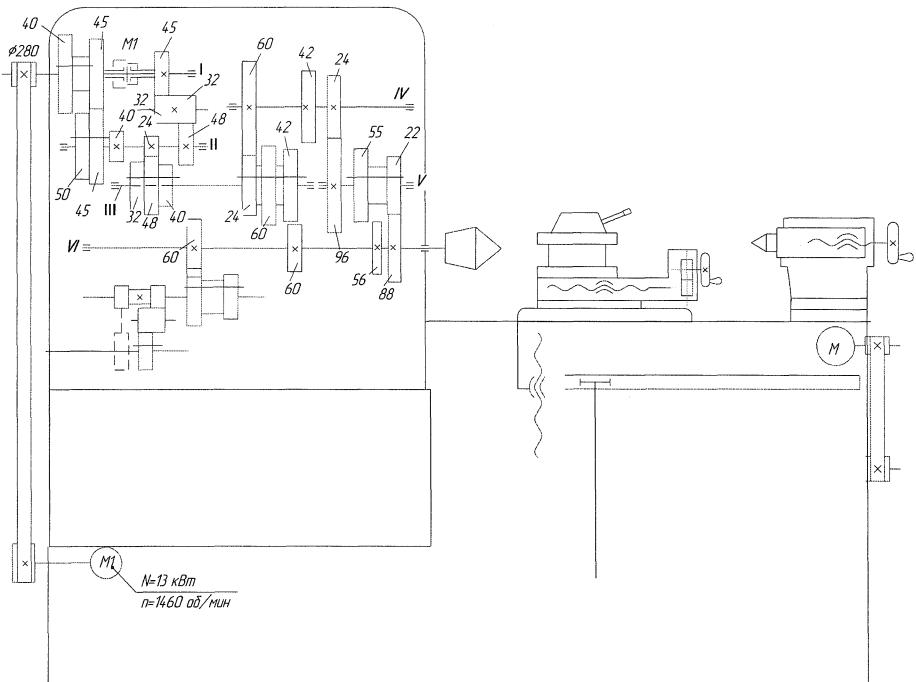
Кинематическая схема коробки скоростей станка 1М63
